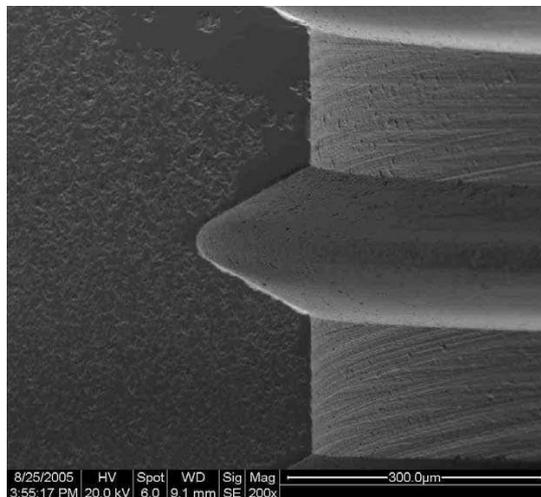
Beispiel für Gewinde; REM Aufnahme Gewinde M1,6 (200x)
